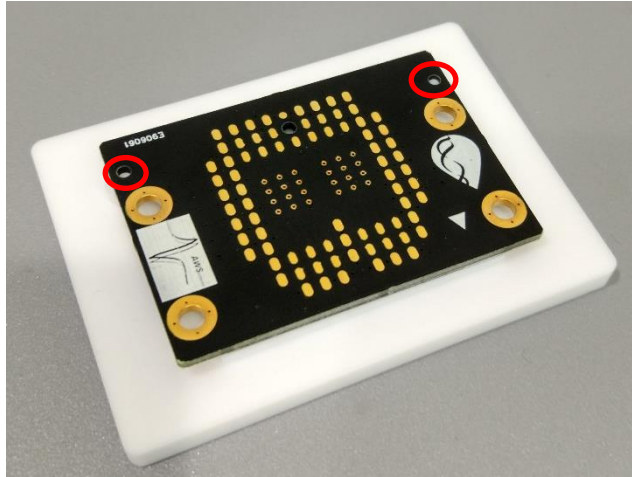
Pieza sobre la que se coloca la lámina de OSTEMER. Marcado en rojo los taladros que permiten colocar la PCB de contactos
